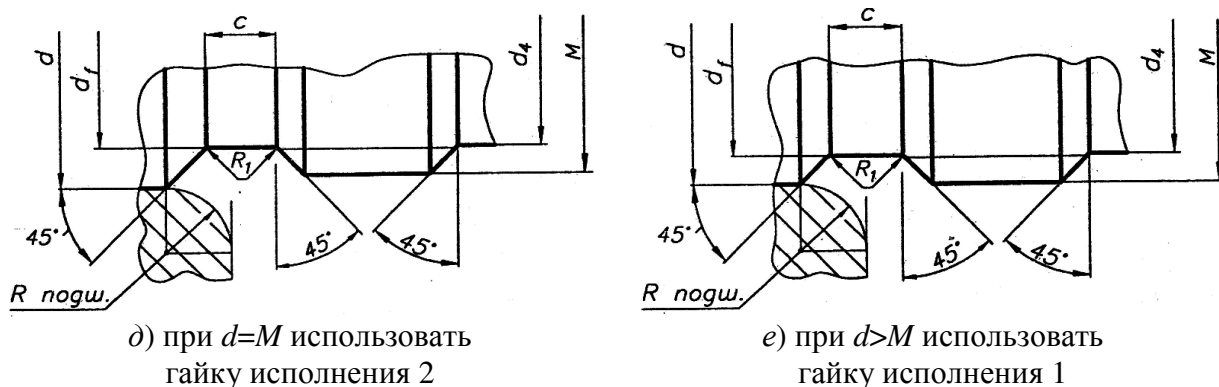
Размеры вала в месте установки гайки и шайбы
